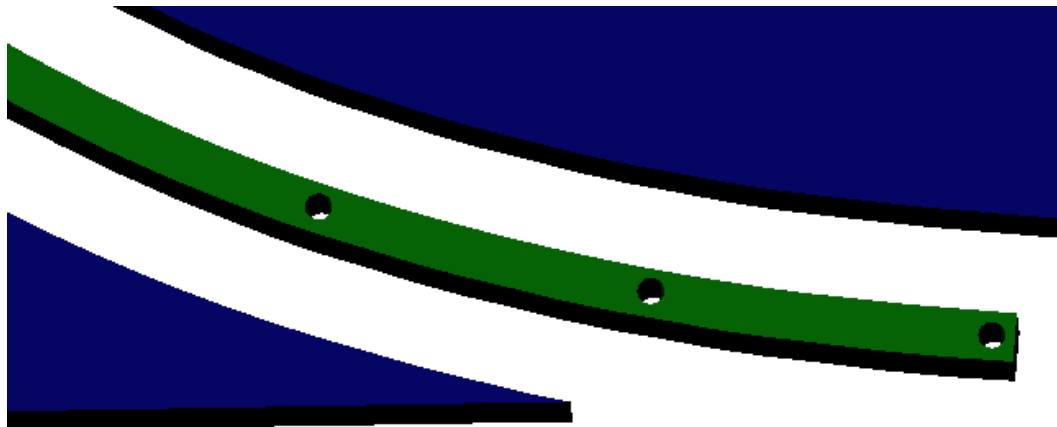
Sección 8a: Resultado de taladrado en detalle
